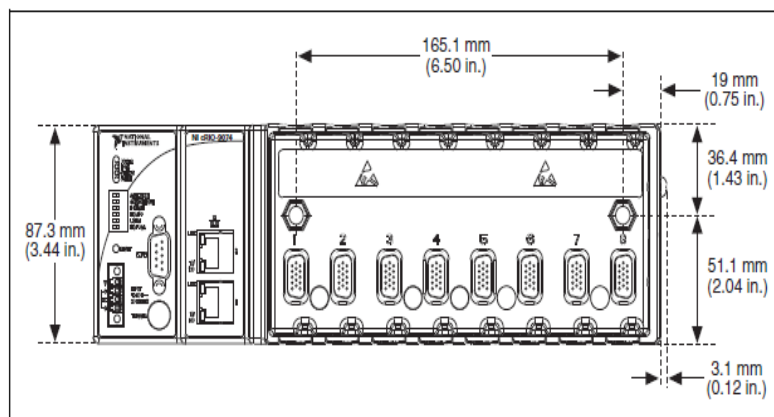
cRIO-9074, Vista Frontal con Dimensiones
